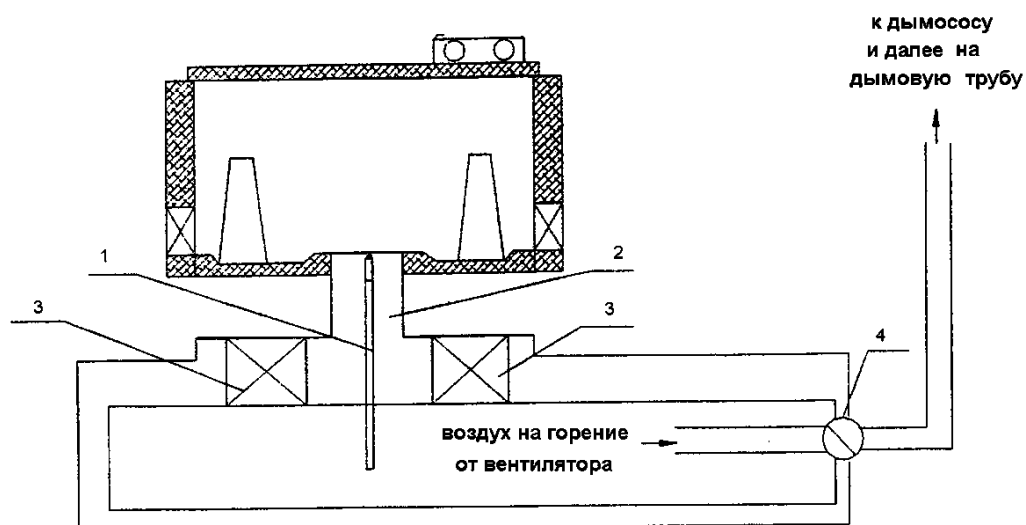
Схема регенеративного нагревательного колодца с отоплением из центра подины: 1 – газоподающая труба с соплом; 2 – горловина; 3 – регенераторы; 4 – дымовоздушный перекидной клапан
